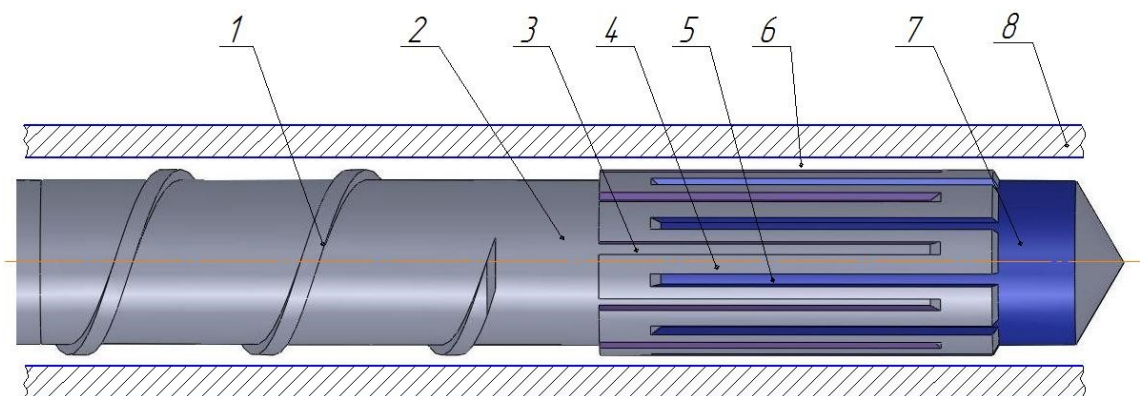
Змішувач бар'єрного типу: 1 – шнекова нарізка; 2 – вхідний кільцевий канал; 3 – вхідне поглиблення; 4 – бар'єрний гребень; 5 – вихідне поглиблення; 6 – зазор між бар'єрним гребенем і корпусом екструдера; 7 – вихідний кільцевий канал; 8 – корпус екструдера
